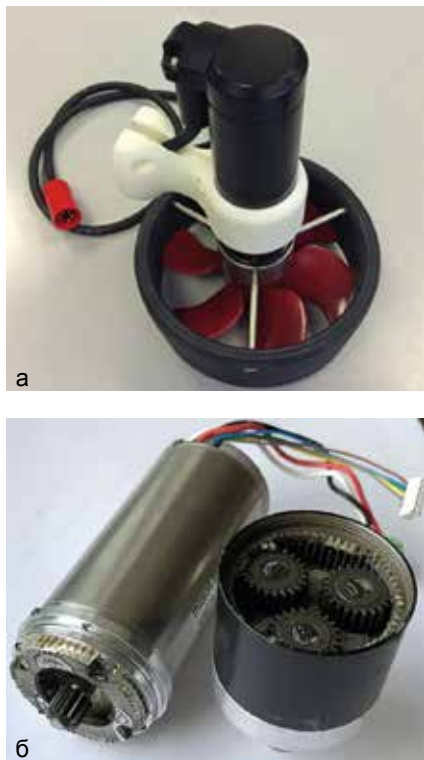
Двигатель ТНПА «Марлин-350»: а – двигатель, вид в сборе; б – электродвигатель и редуктор из состава двигателя
